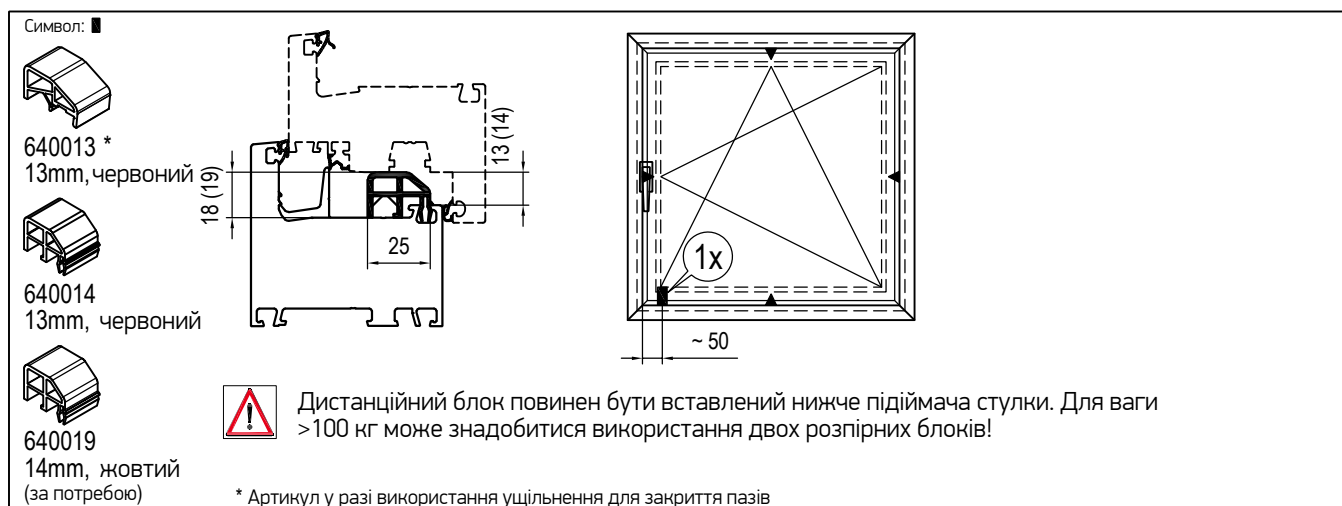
Дистанційний блок 13(14)мм як допоміжний засіб для виготовлення конструкції
